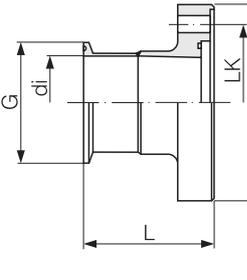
Dimensioni vista frontale del sensore DN 40...100
